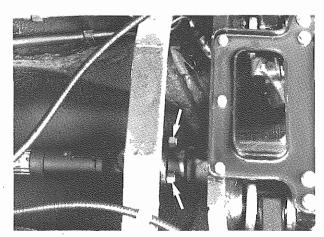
Viti fissaggio albero di trasmissione sulla flangia post. Screws fixing propeller shaft on rear flange
